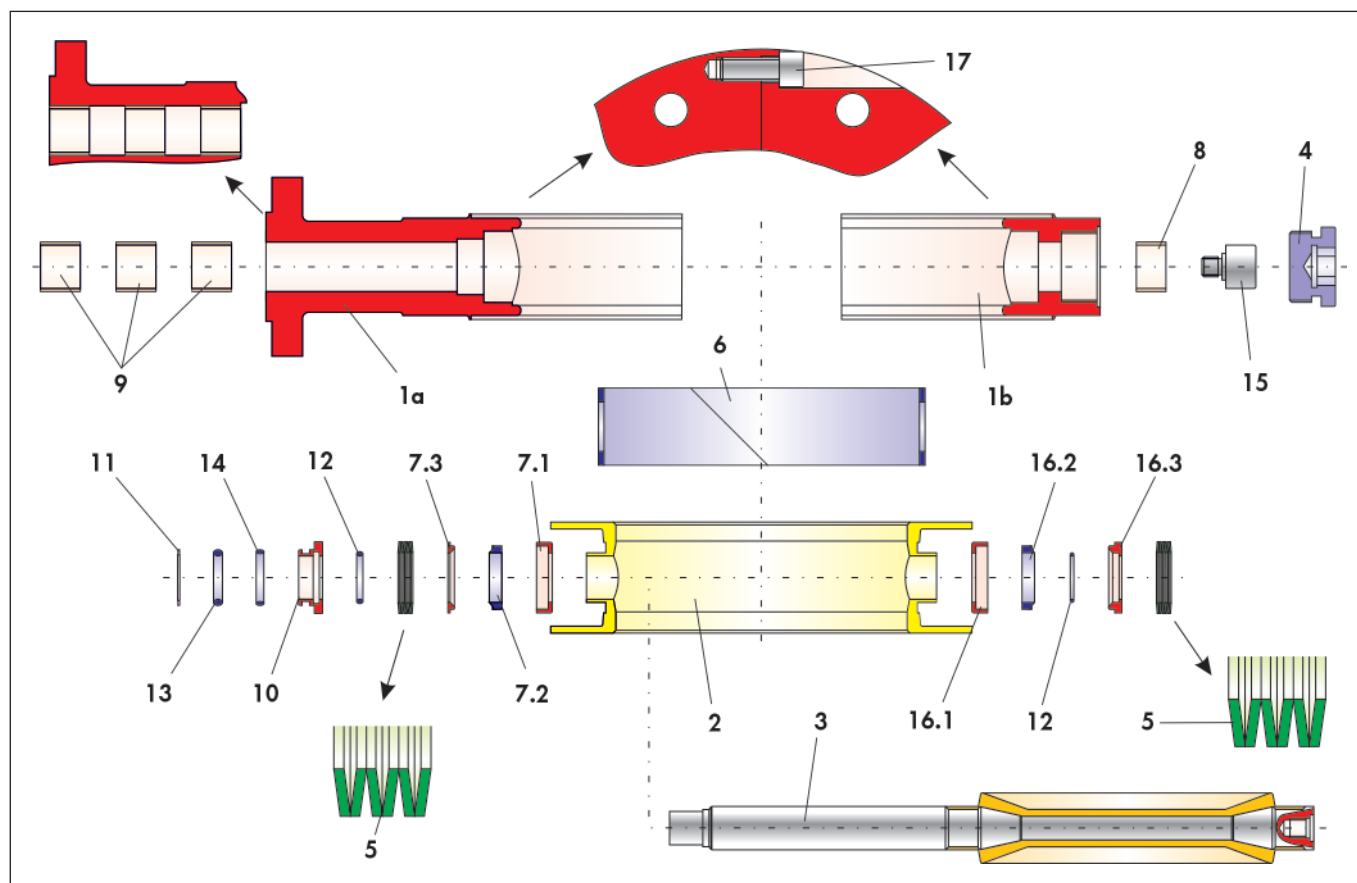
Сборочный чертеж заслонки BR 10e
